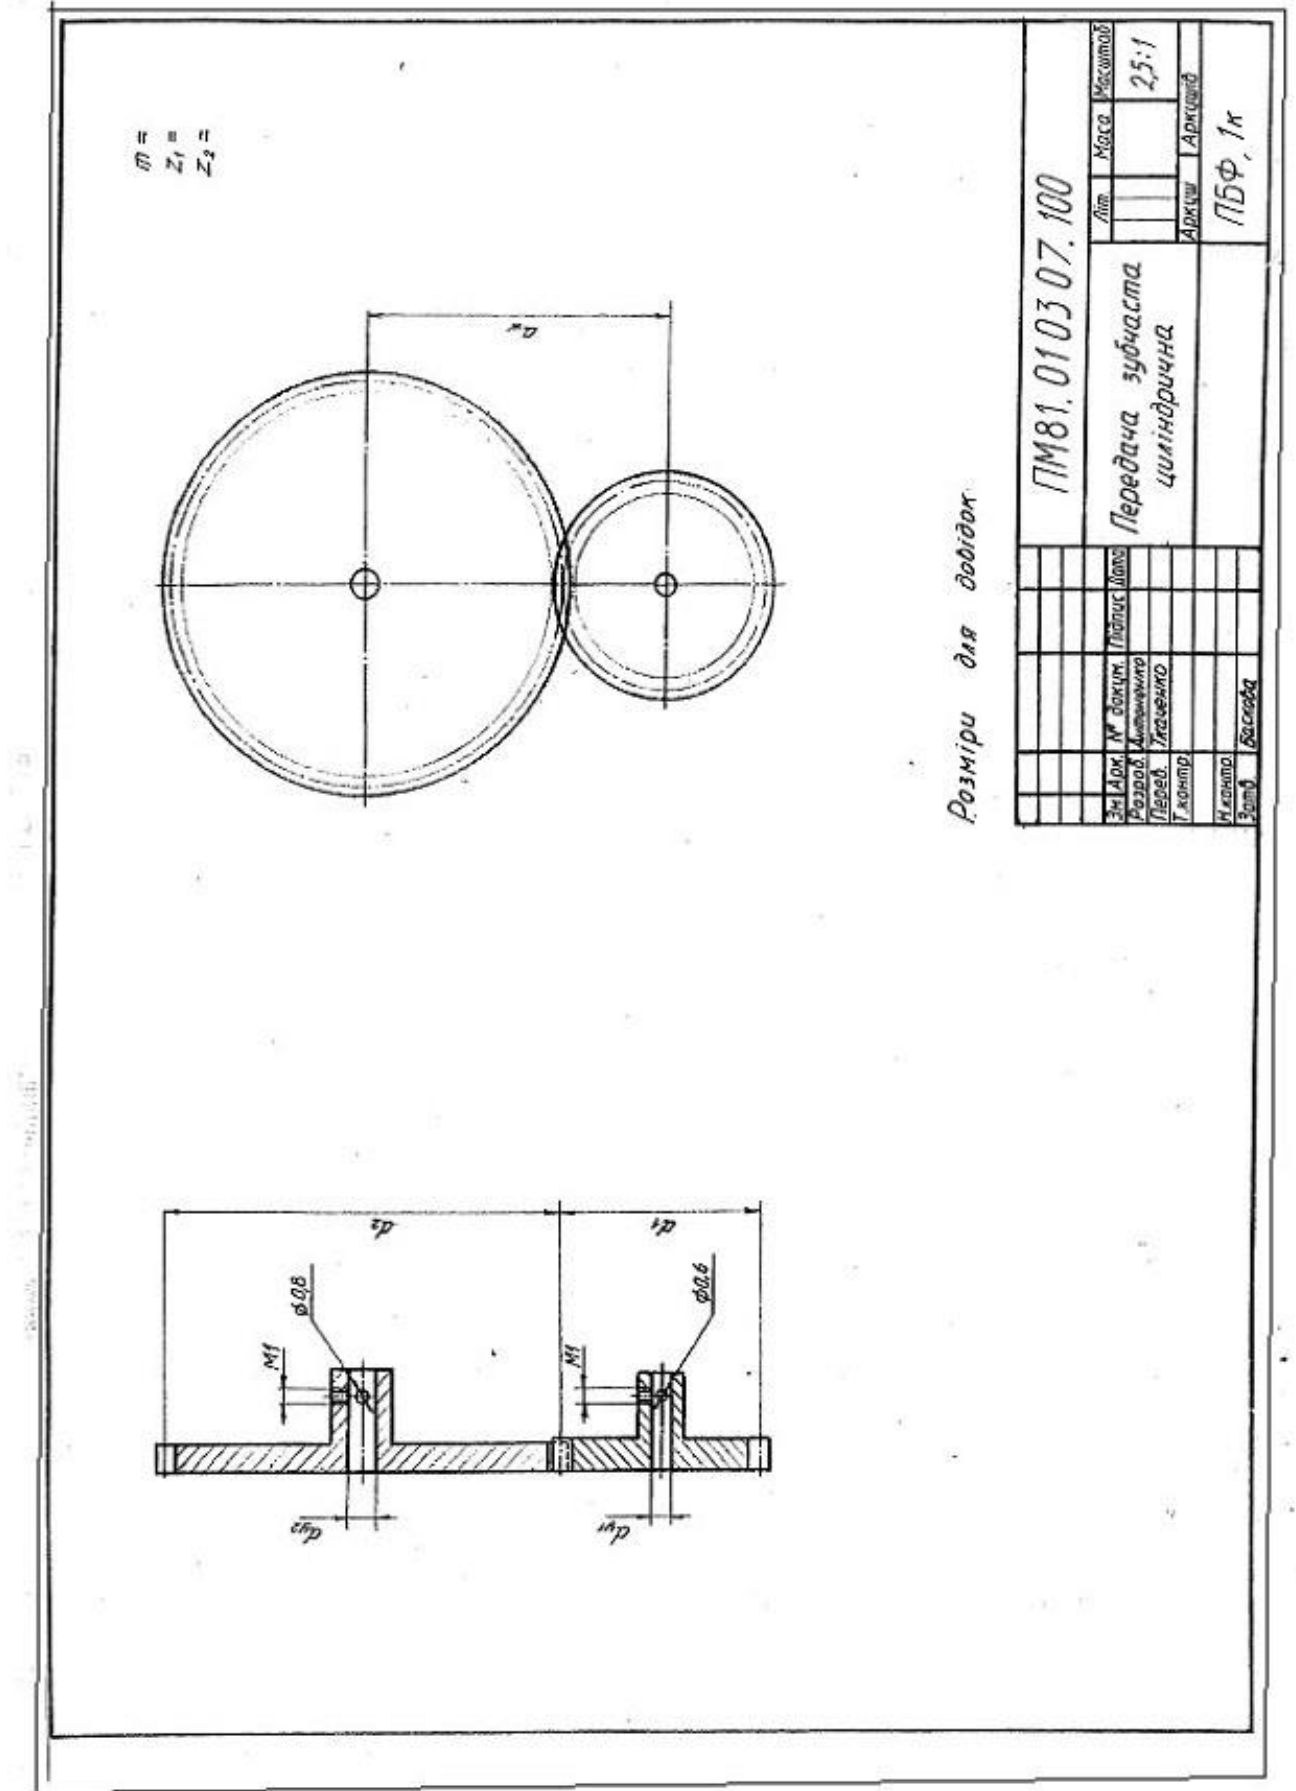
Кресленик циліндричної зубчастої передачі
